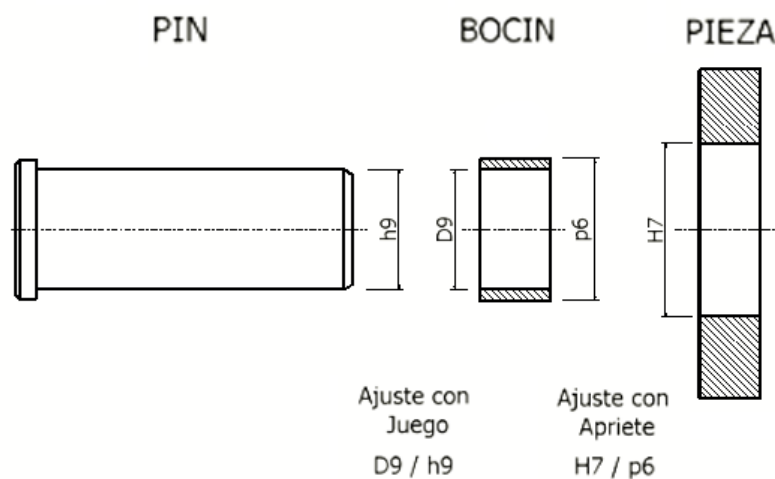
Ensamblado de cojinetes de deslizamiento con ajustes y tolerancias
